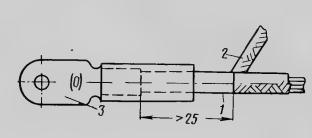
Установка бандажа на экранирующие плетенки пучка экранированных проводов:
